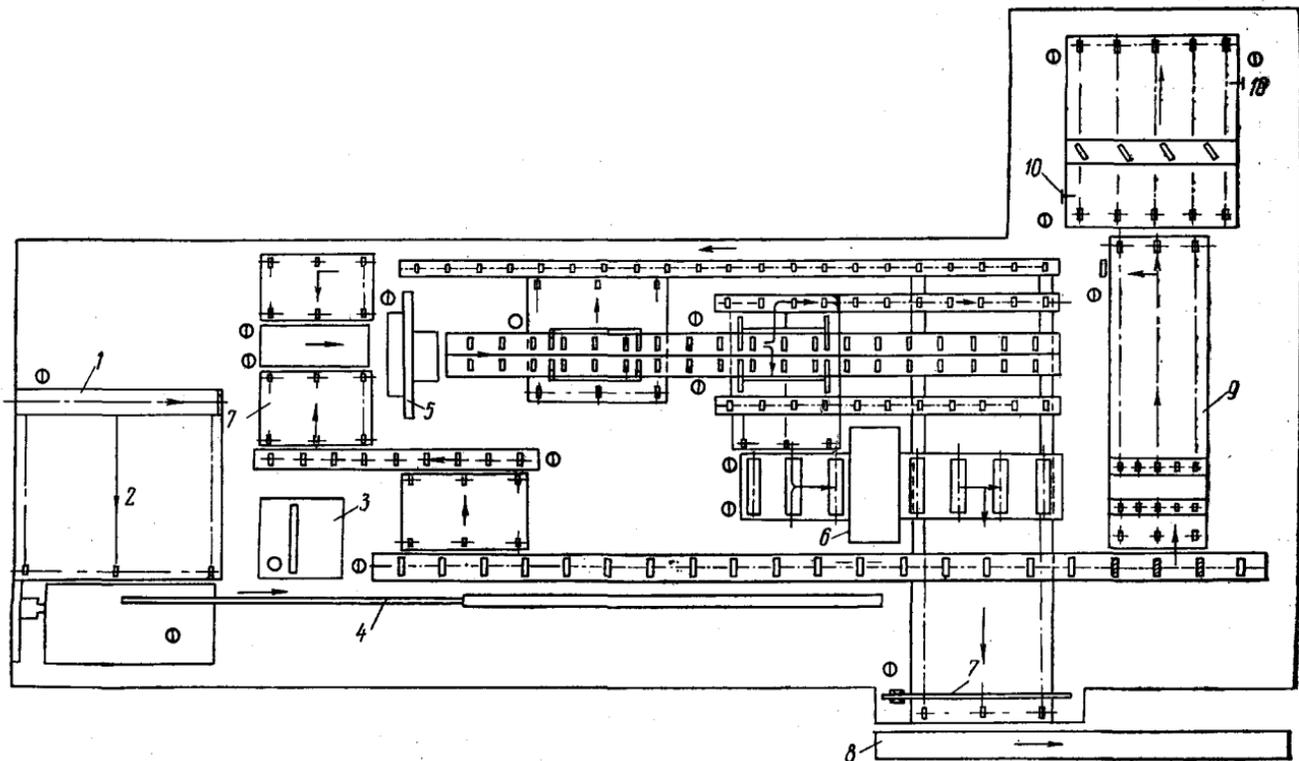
План лесопильного цеха, оборудованного ленточнопильными станками:
